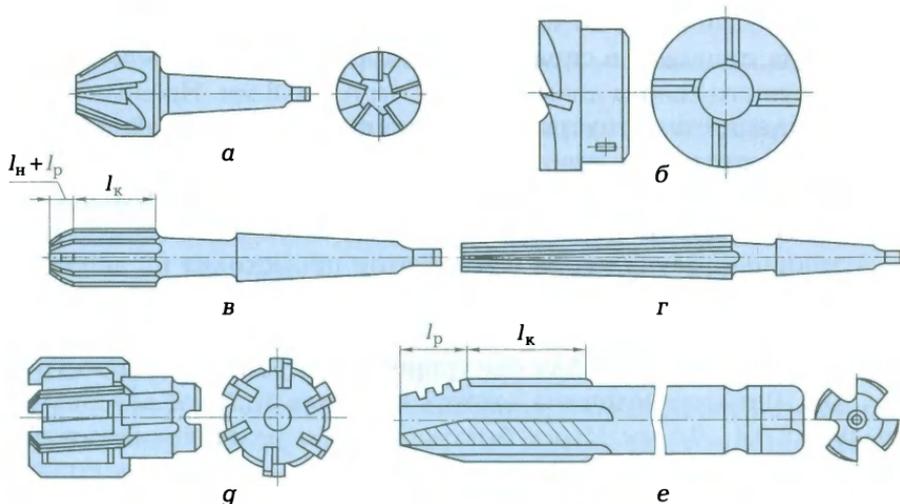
Инструменты для обработки отверстий на сверлильных станках: *а, б* — зенкеры; *в, г, г* — развертки; *е* — метчик;  $l_n$ ,  $l_p$ ,  $l_k$  — соответственно направляющая, режущая и калибрующая части
